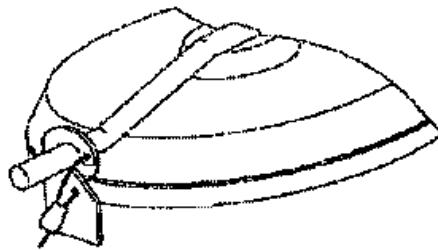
Схема установки универсального ЗПУ с длиной каната 300 мм на крышке загрузочного люка вагона-хоппера для перевозки цемента модели 19-12-1217 постройки "Рузхиммаш"
